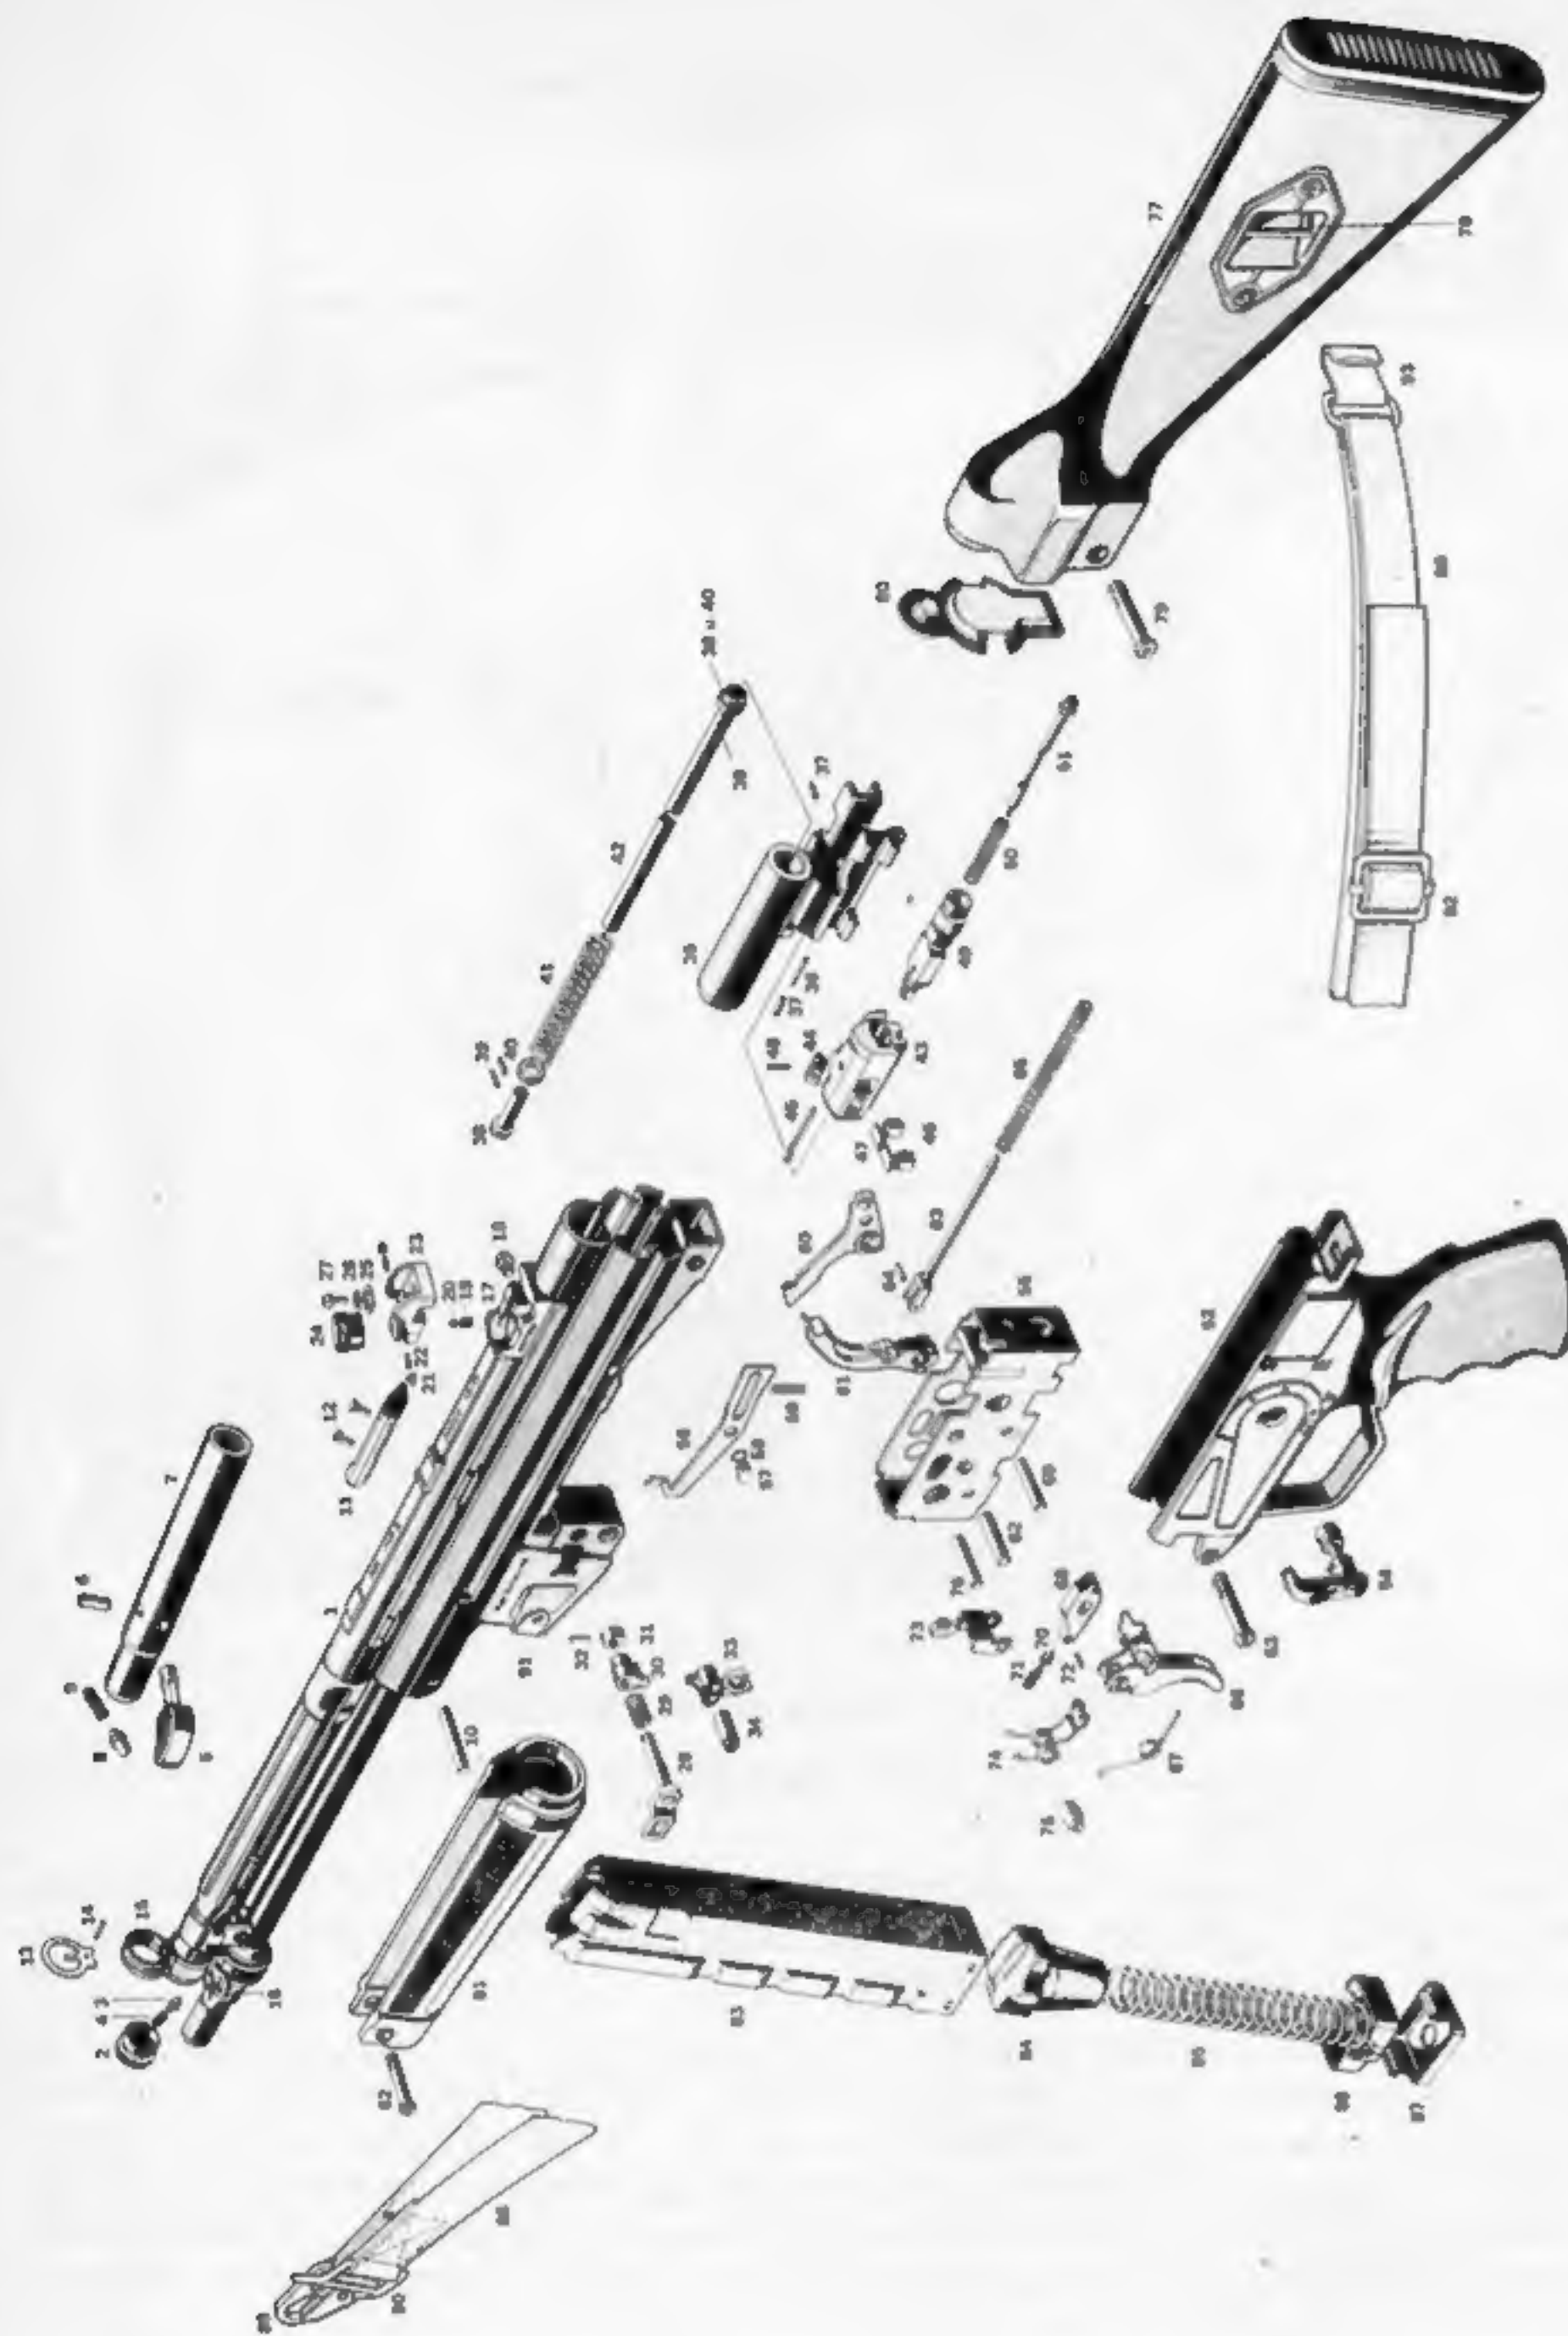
Explosionszeichnung der MP 5 A2 (Teileverzeichnis)
